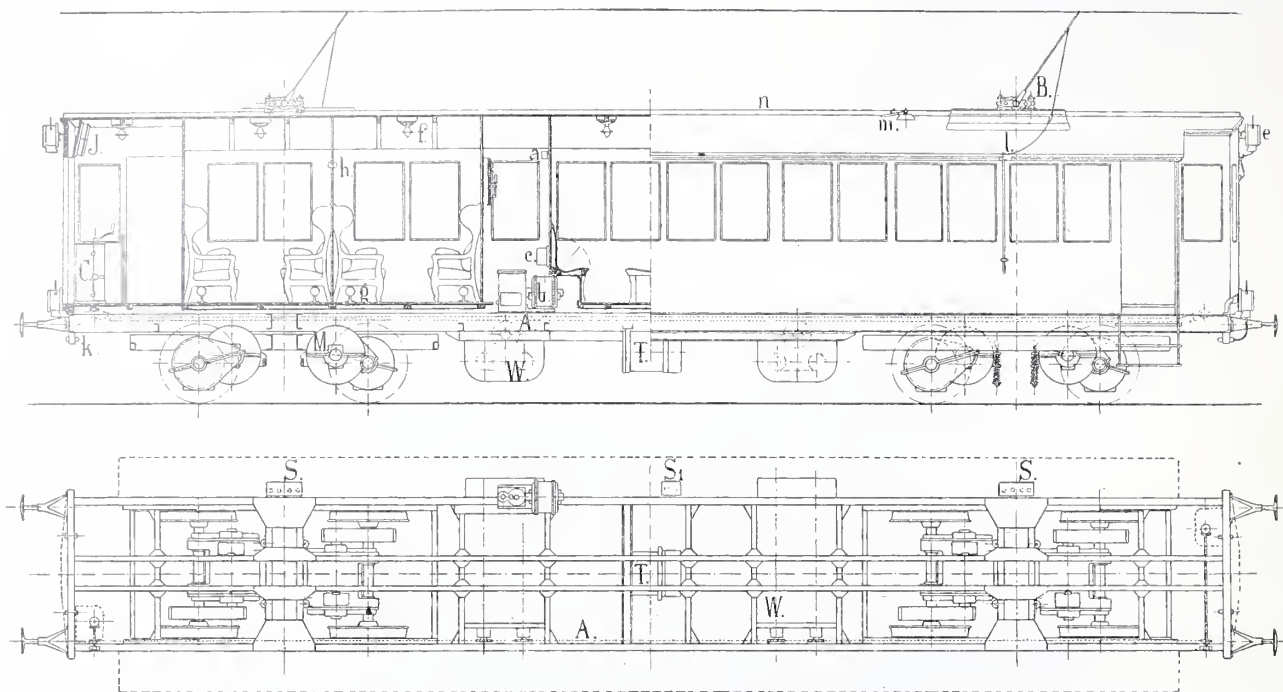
Ansicht und Grundriss. 1:100.
